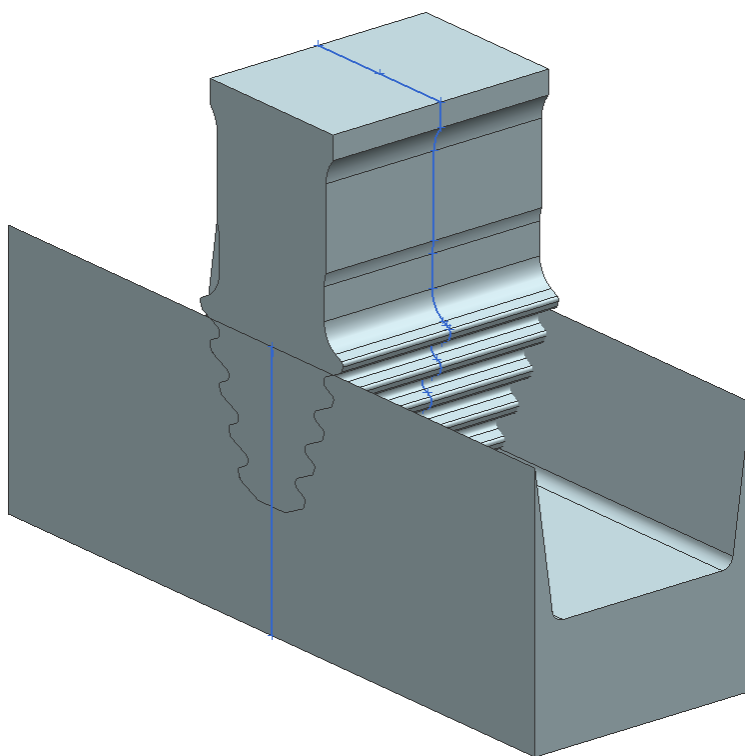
Объем-заготовка ножки и вспомогательный объем для ее усечения
